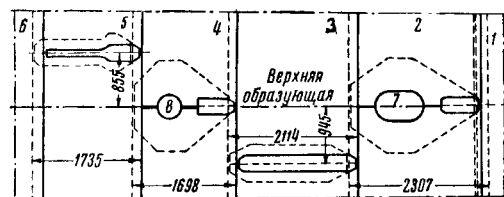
Заклёпочные швы цилиндрической части котла паровоза серии ФД: 1—второй барабан; 2—третий барабан; 3—наружная накладка; 4—внутренняя накладка; 5—сварной участок
